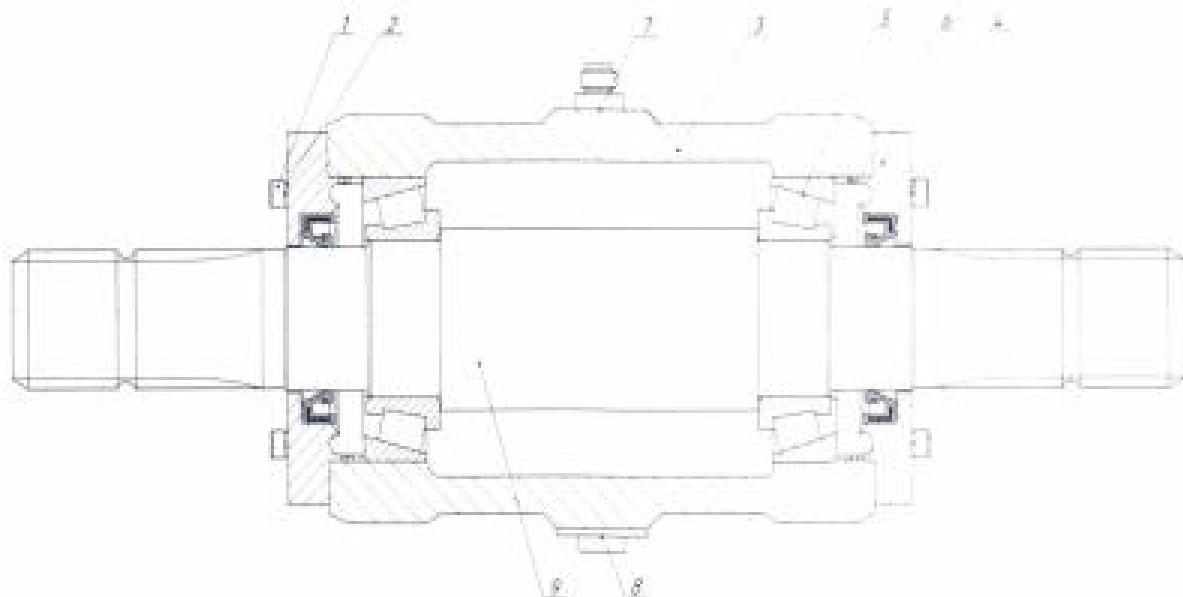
Опора: 1 – болт; 2 – шайба; 3 – кришка; 4 – манжета; 5 – підшипник; 6 – корпус; 7 – віддашна; 8 – пробка; 9 – вал
